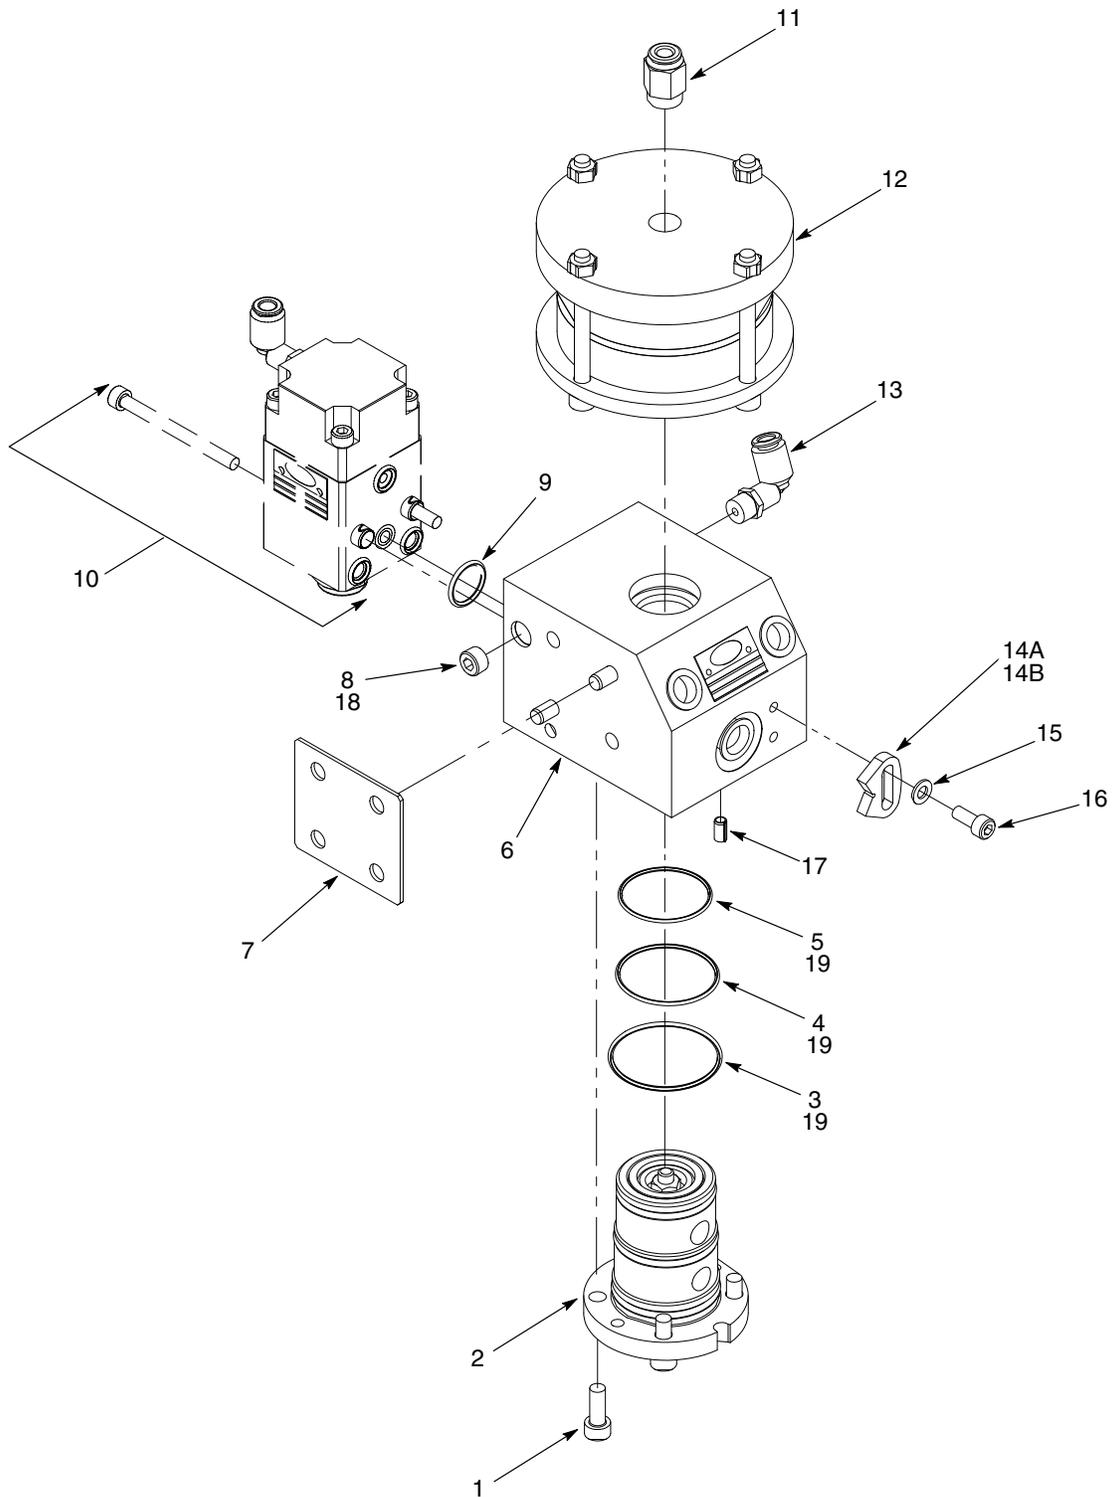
Pièces du régulateur CP II – 240 V chauffé
